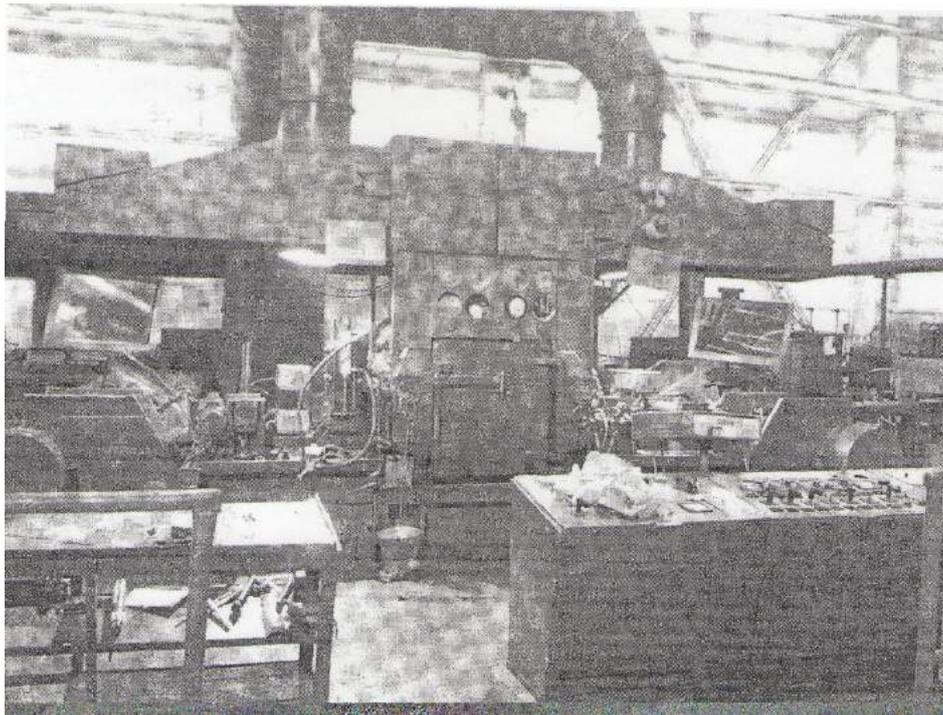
Реверсивный 20-ти валковый стан ЦЛХП
